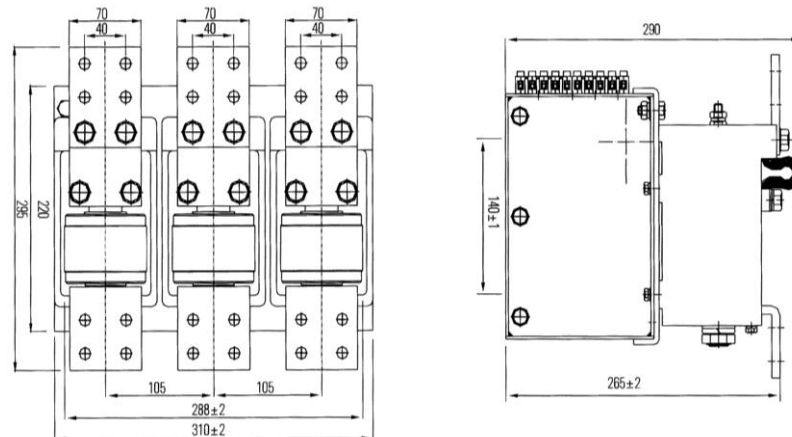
Габаритные размеры КВТ-1,14-1000/1250
